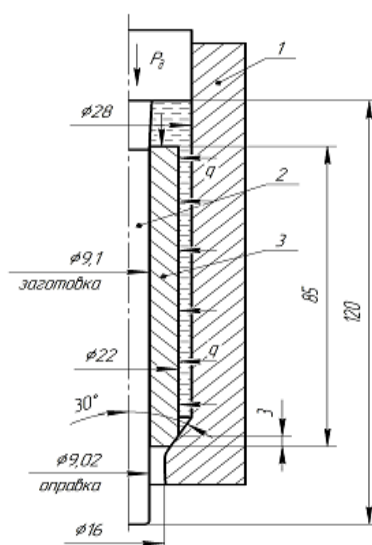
Расчётная схема гидропрессования трубчатых заготовок на оправке
